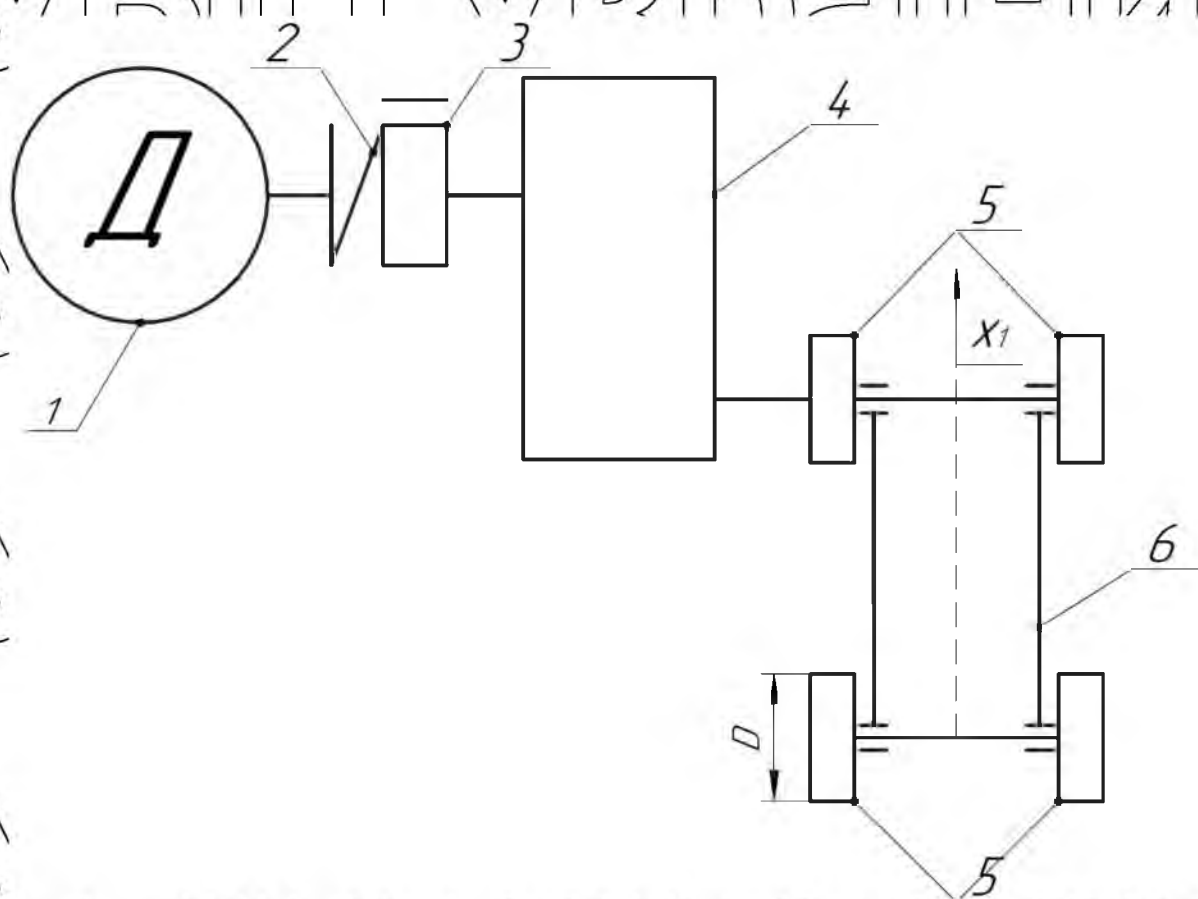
Кінематична схема приводного механізму електротрактора
